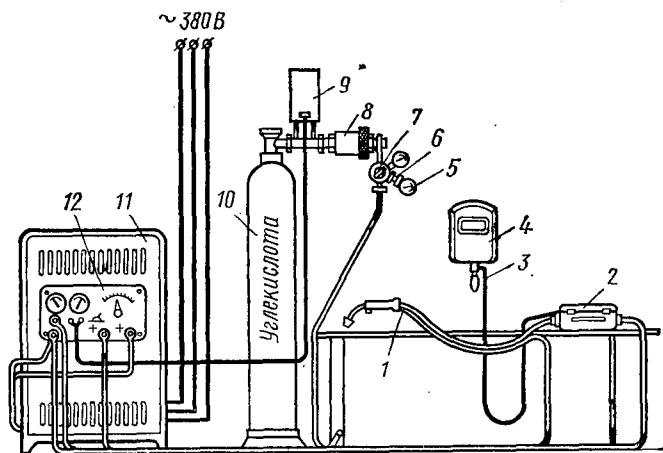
Схема поста для сварки в среде углекислого газа
